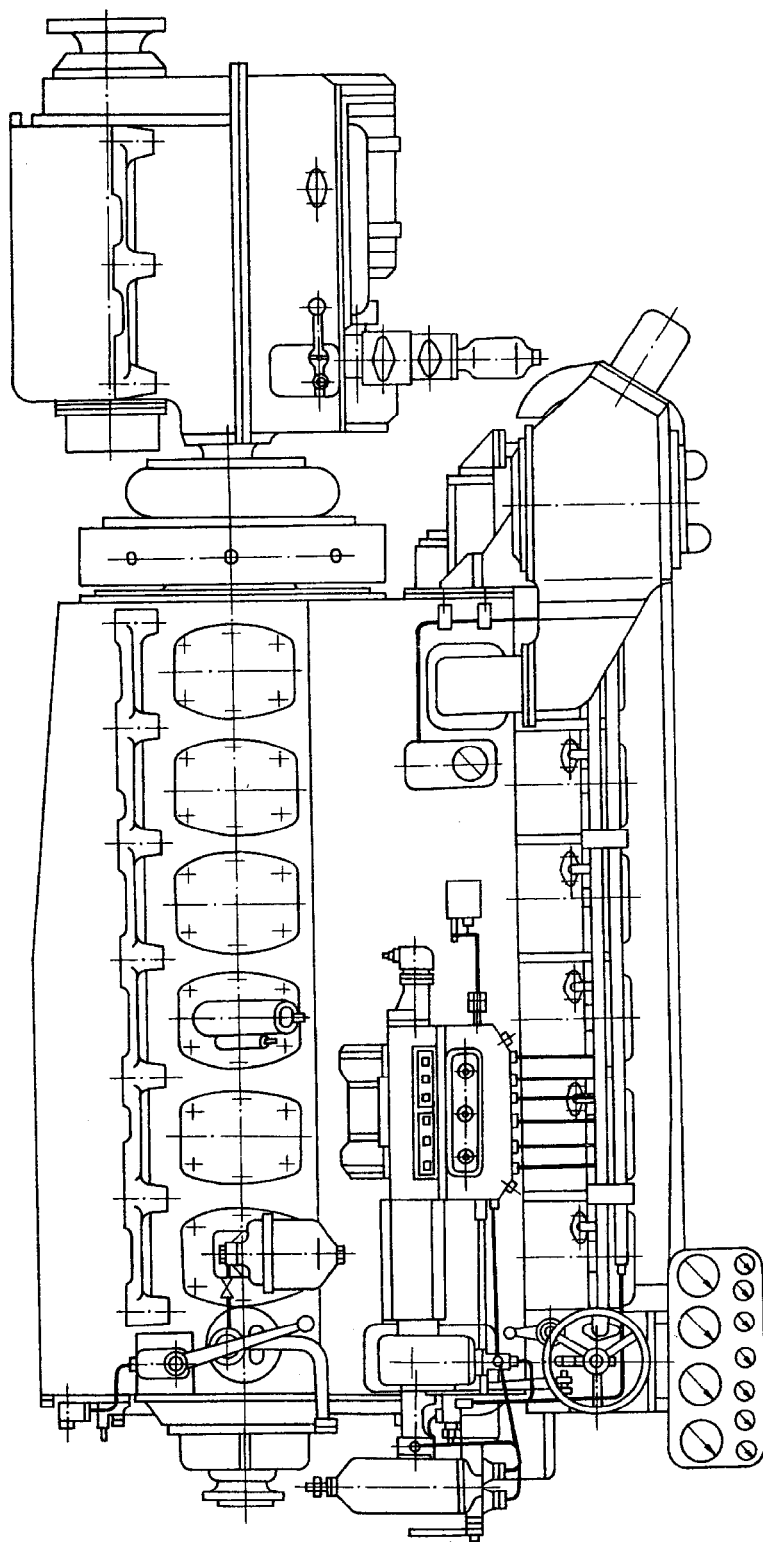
Дизель-редукторный агрегат 6ЧСПН2А 18/22-225-1 /общий вид/
